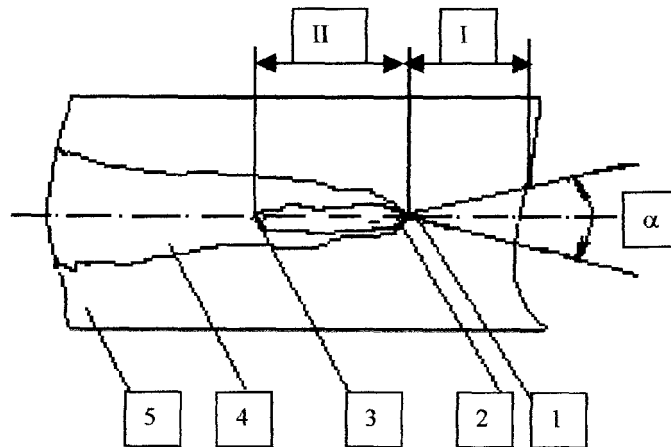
Схема ділянки високочастотного зварювання труби.
